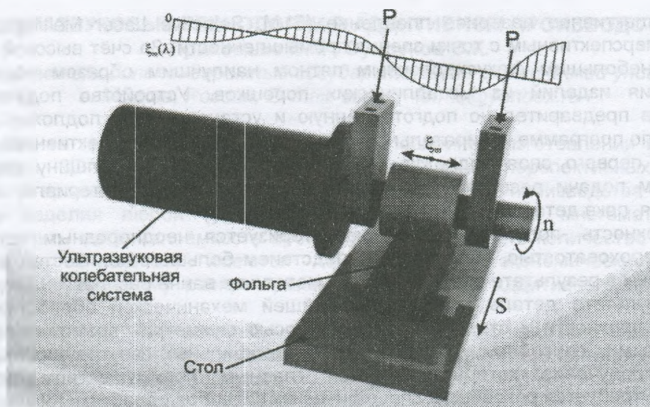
Схема ультразвуковой сварки алюминиевой фольги
